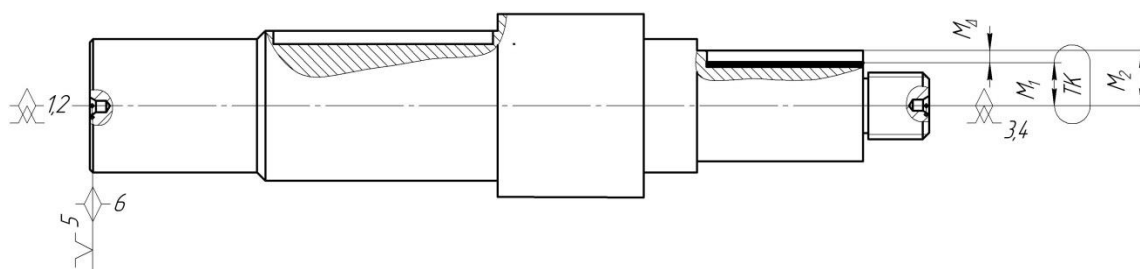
Базування вала (перший варіант) при обробці шпонкового вала
